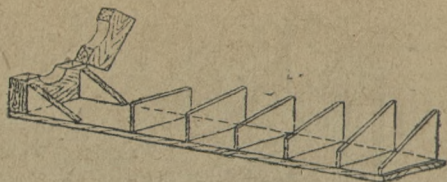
Облегченное приспособление для проверки установочных углов лопасти после правки
